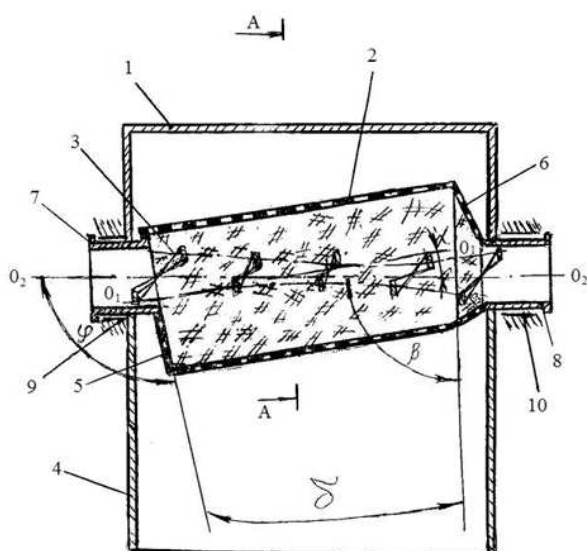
Установка для выделения жидкой фракции из материалов, вид спереди
